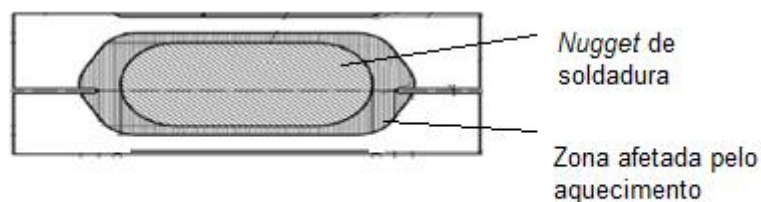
Ponto de Soldadura na interceção de duas chapas
